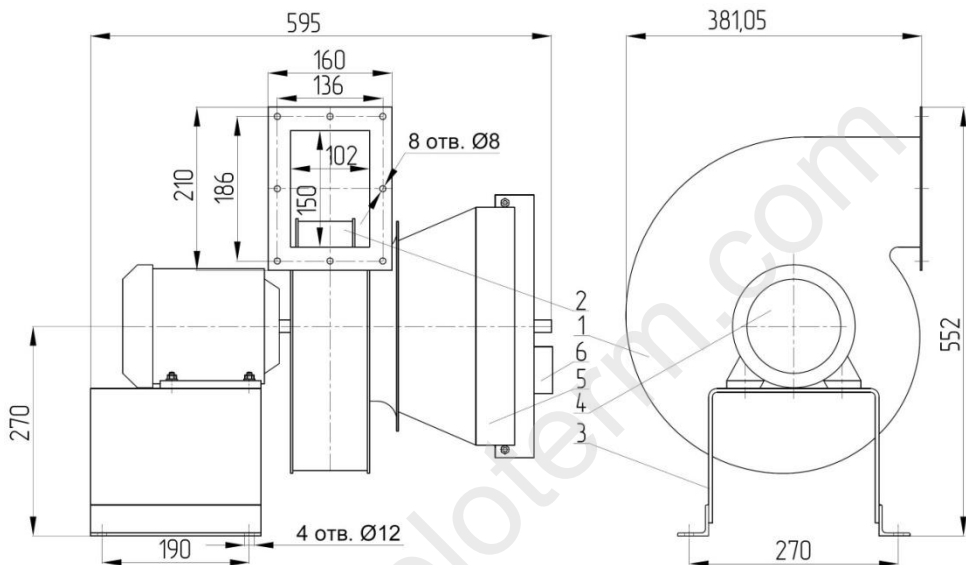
Вентилятор ВД-2,7 (1- корпус, 2-рабочее колесо, 3-рама, 4-эл. двигатель, 5- шибер, 6- привод шибера.
